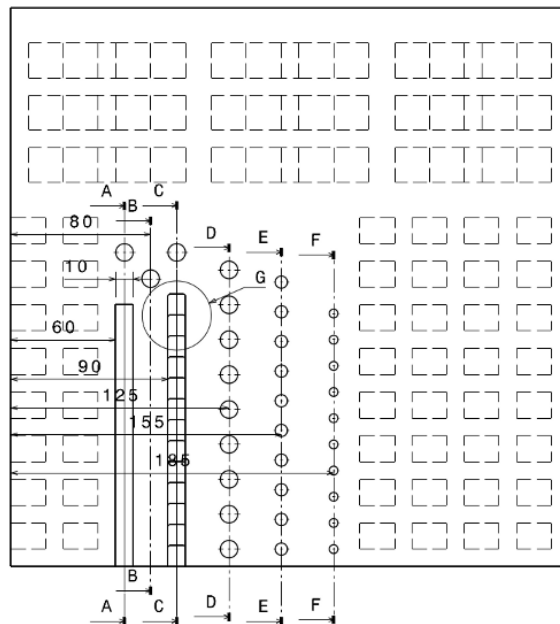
Mechanische Bearbeitung: Positionierung Schnittebenen
